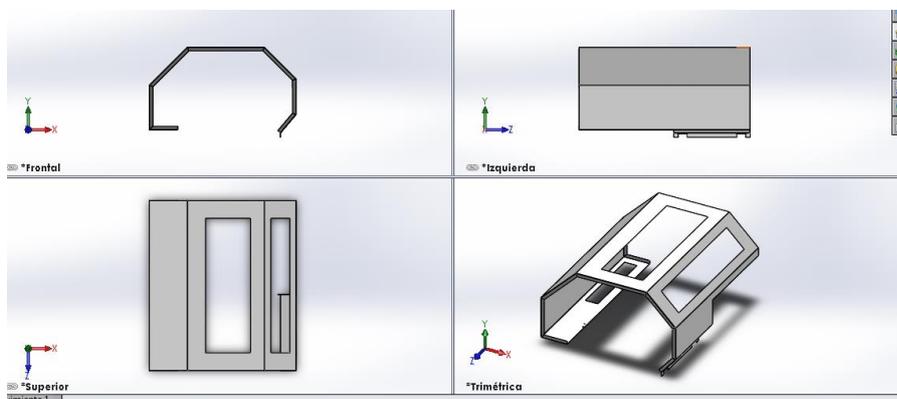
Diseño CAD de la cubierta protectora de seguridad
